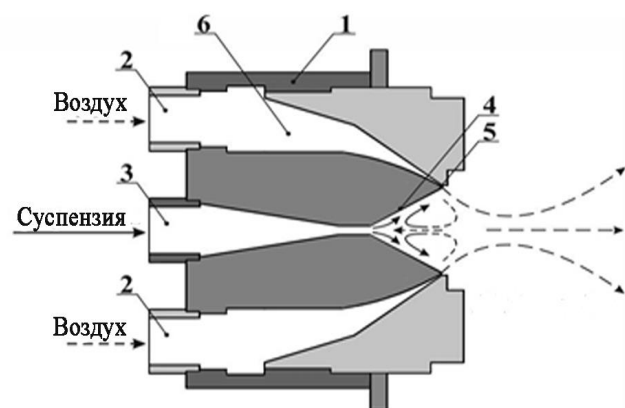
Схема пневматической форсунки: 1 – корпус; 2 – патрубок для подачи газа; 3 – труба для подачи жидкости (водоугольной суспензии); 4 – диффузорное сопло; 5 – кольцевое газовое сопло; 6 – газовая камера.
